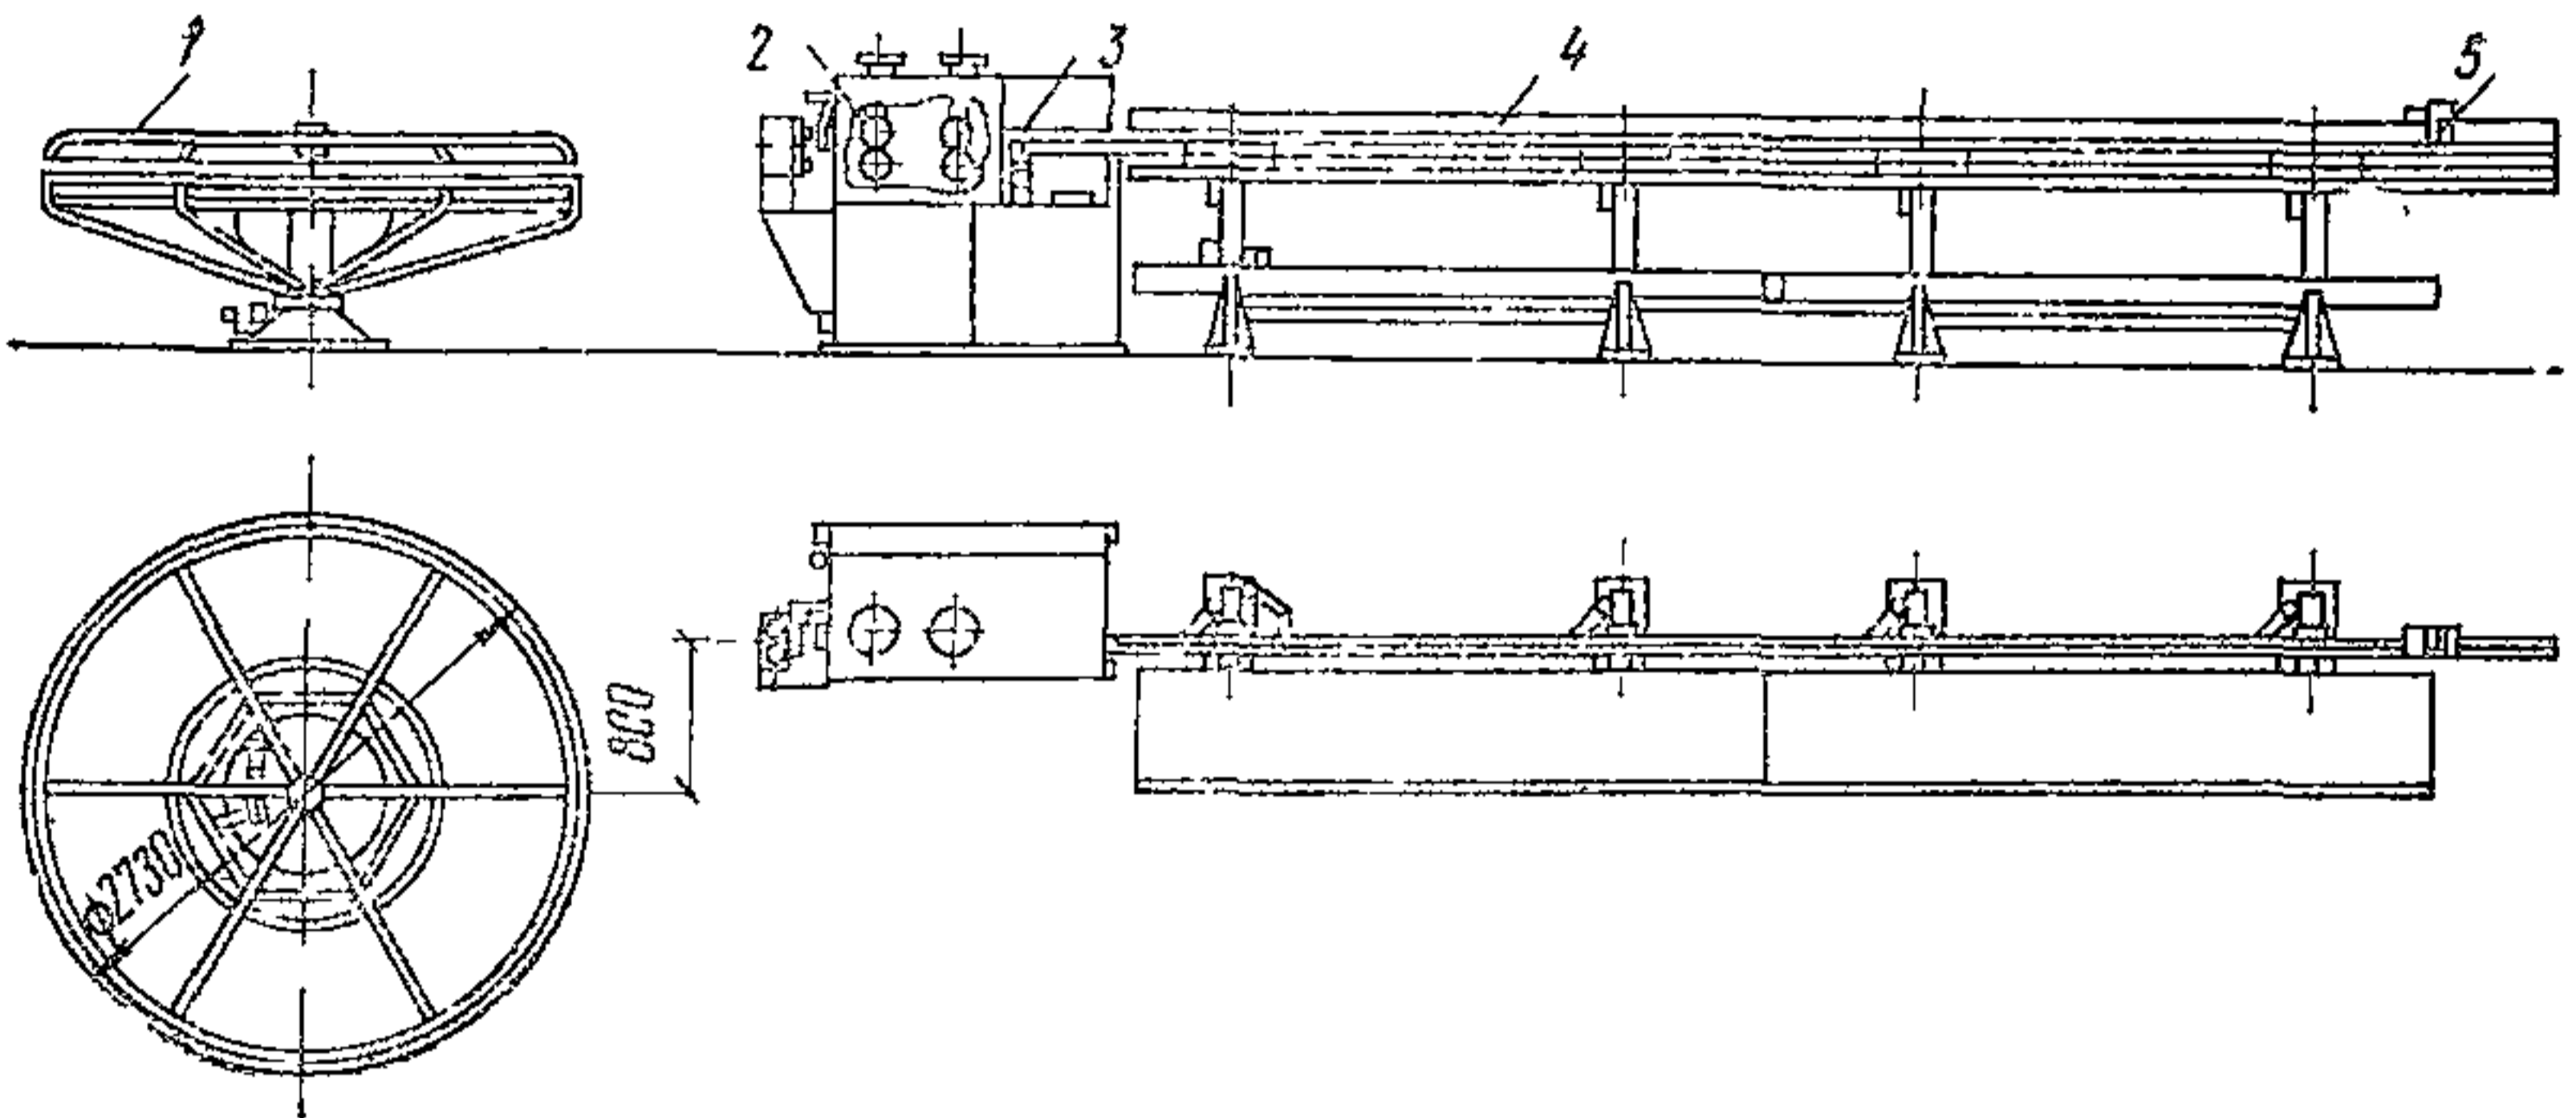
Линия заготовки высокопрочной проволоки и прядей СМЖ-213
